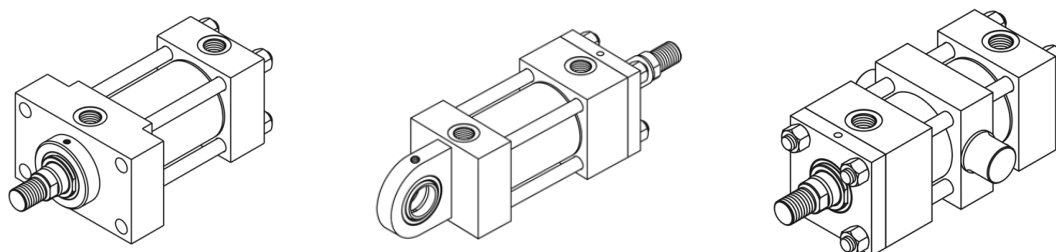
Dvojičinné provedení hydraulického válce:
